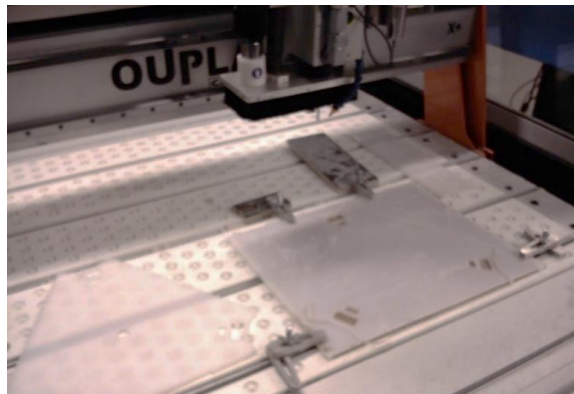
Corte dos painéis do chassis, em polietileno, por maquinagem CNC.
